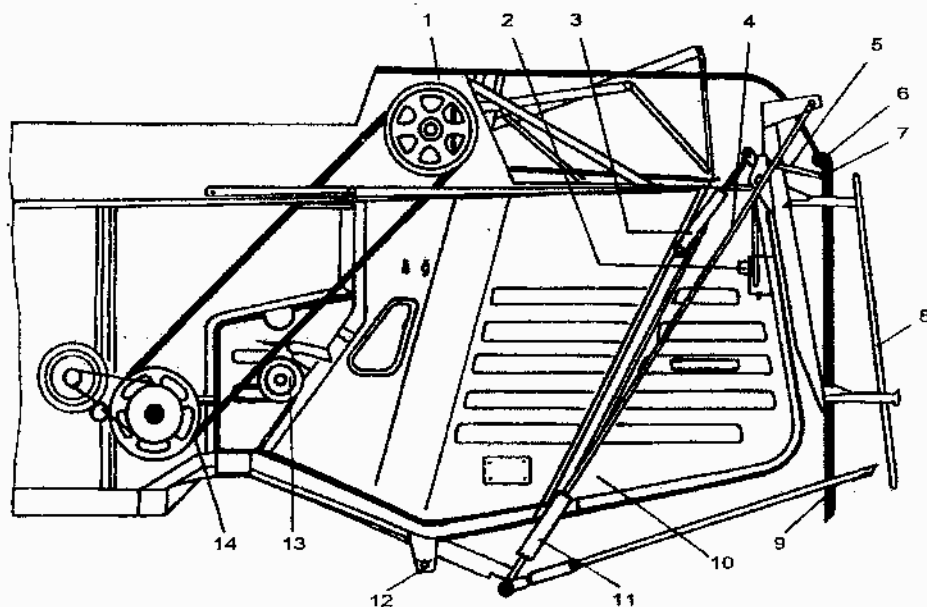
Копнитель навесной гидрофицированный (вид слева):
